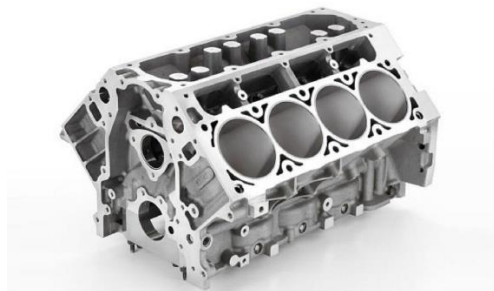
Bloque motor integral. Fuente: ActualidadMotor [18]
